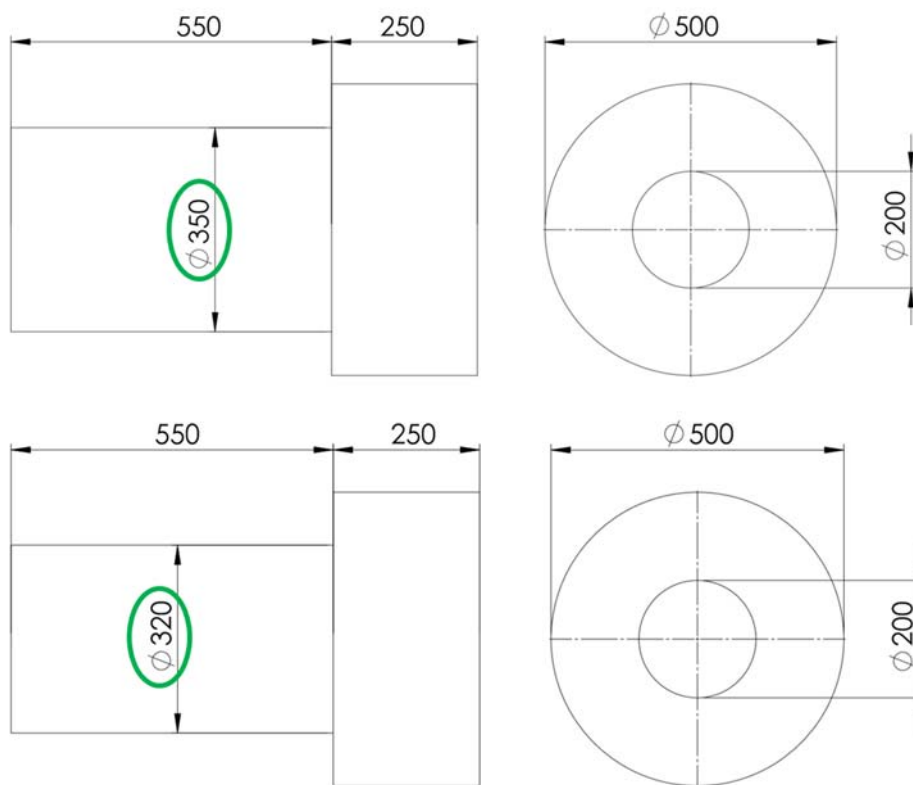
Adaptación del soporte interno a las dimensiones de los rodamientos seleccionados
